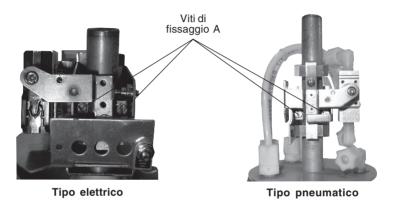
Meccanismo interruttore elettrico e pneumatico
